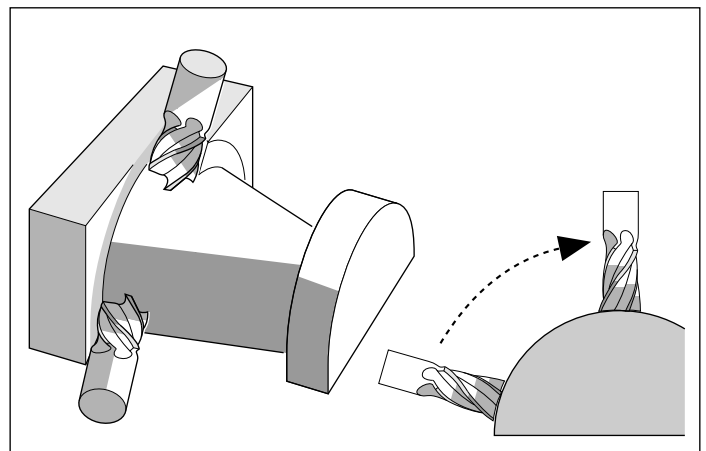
Gleichzeitiges Verfahren von mehr als drei Koordinatenachsen, z.B. Bearbeiten einer 3D-Form mit Schaftfräser
